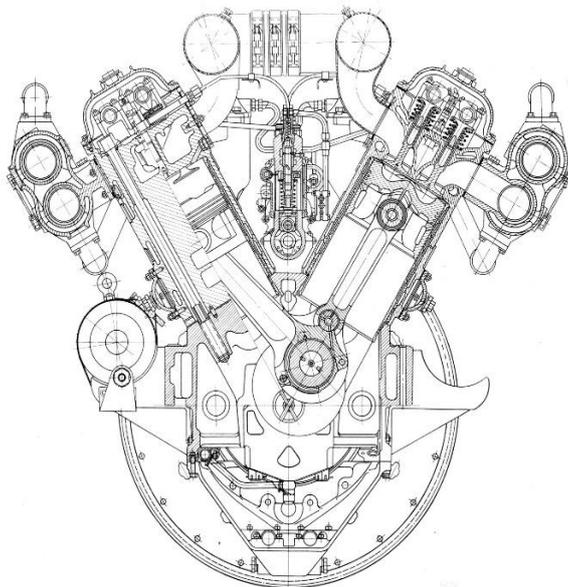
Схема конструкции V-образного двигателя внутреннего сгорания.
